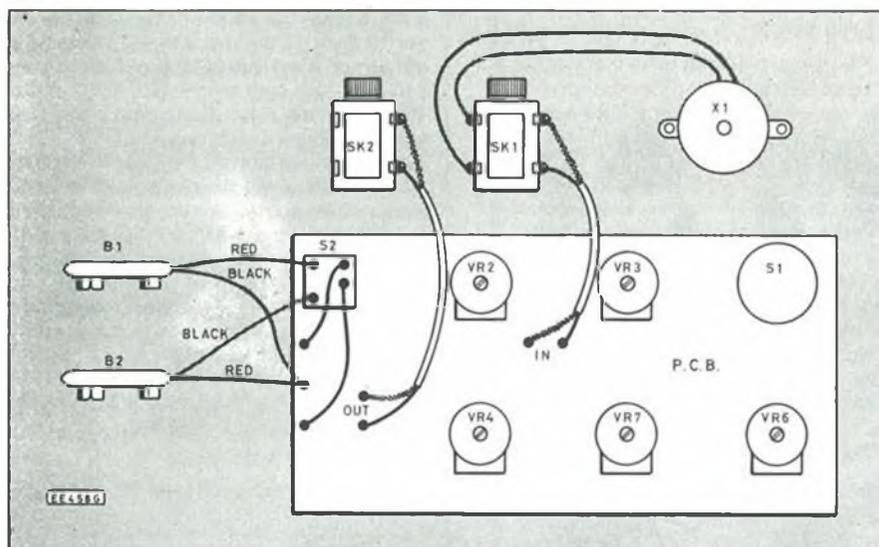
Particolari dei cablaggi delle prese jack, dei connettori delle batterie e del trasduttore piezoelettrico. Nella fotografia è illustrato il circuito stampato completamente montato e fissato sul retro del pannello frontale.
